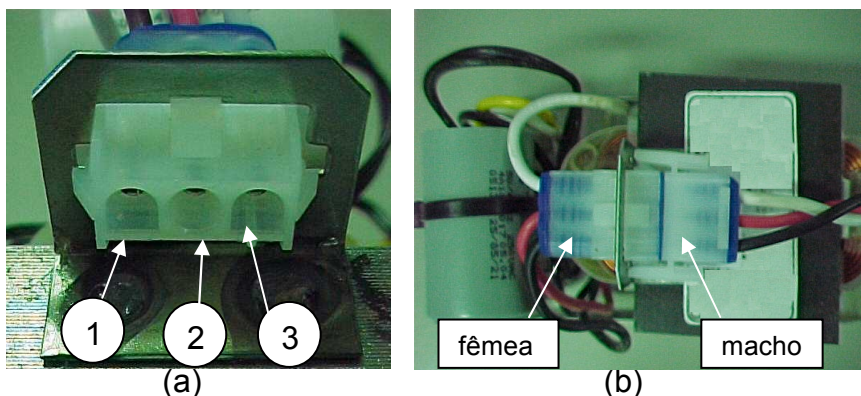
Detalhe do conector (fêmea) no Kit Removível
